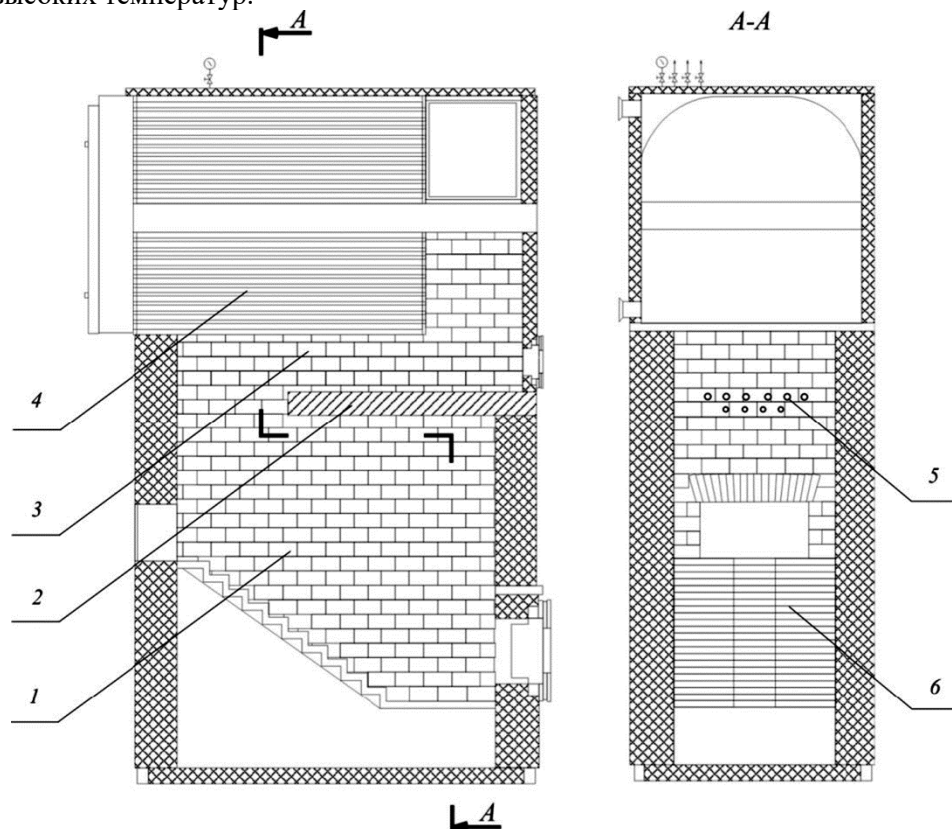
Устройство твердотопливного водогрейного котла КВУ-2000: 1 – топка; 2 – арочный свод; 3 – камера дожига; 4 – двухходовой газовойодяной теплообменник; 5 – сопла вторичного воздуха; 6 – колосниковая решетка
